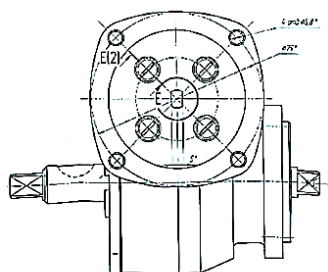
Загальний вигляд малого одноступінчастого черв'ячного редуктора
